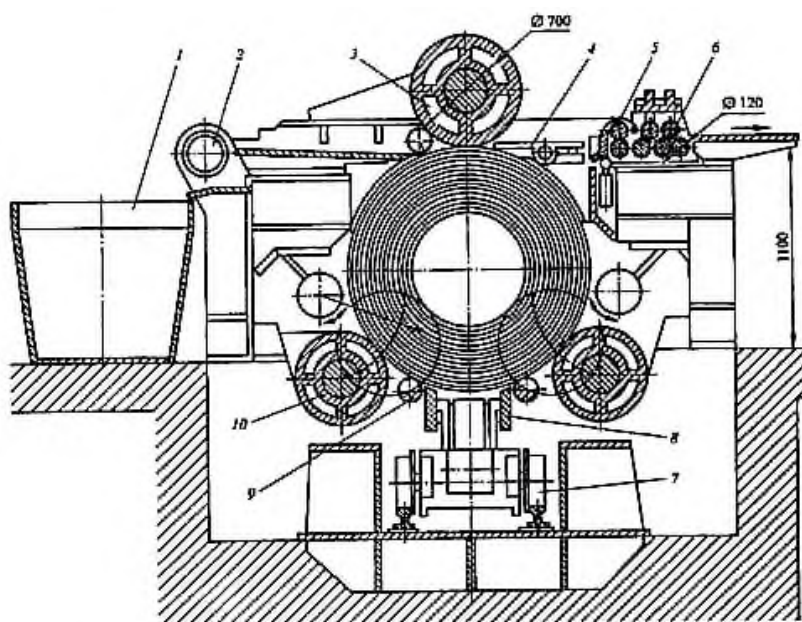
Полуавтоматический разматыватель рулонов [14]
